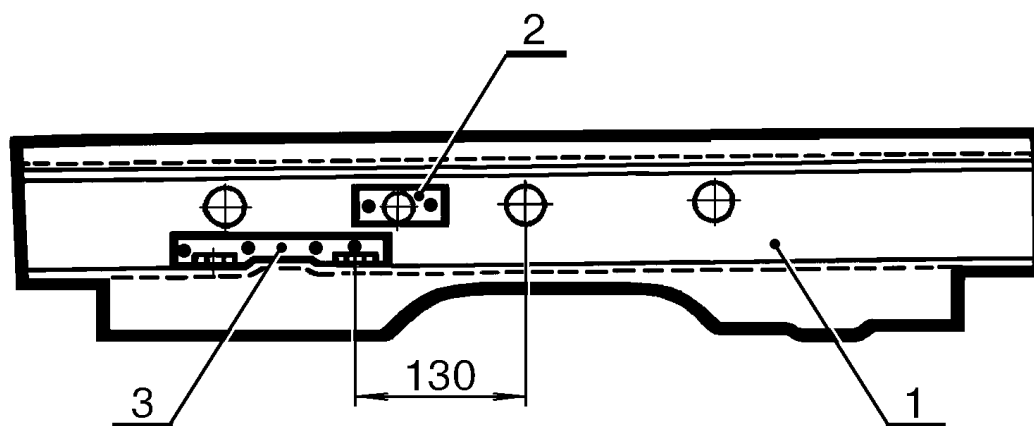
Детали усилителя щитка передка нижнего в сборе. Номера и наименования деталей, количество и шаг сварочных точек приведены в таблице 21 (всего 9 точек).
